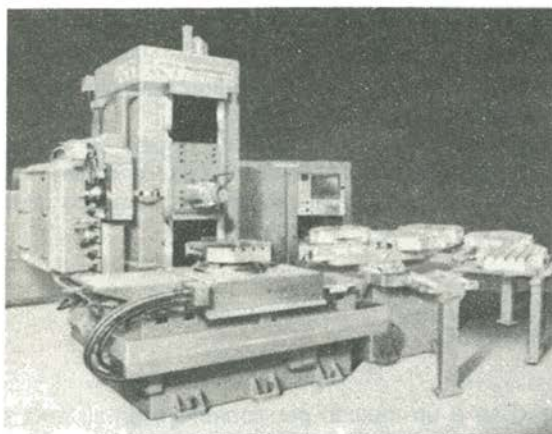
Macchina CN Kearney & Trecker (Per concessione della Kearney & Trecker Corporation)
